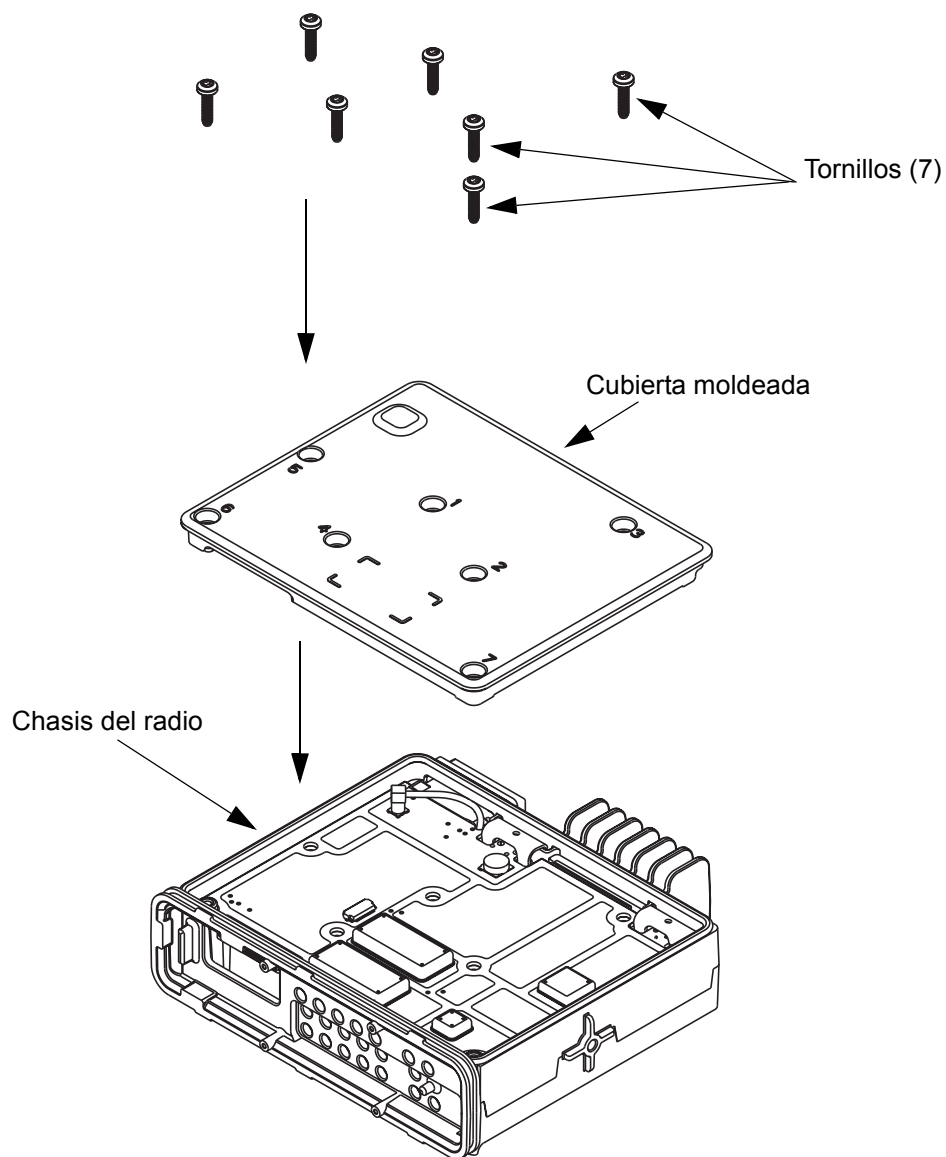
Montaje de la cubierta moldeada sobre el chasis
